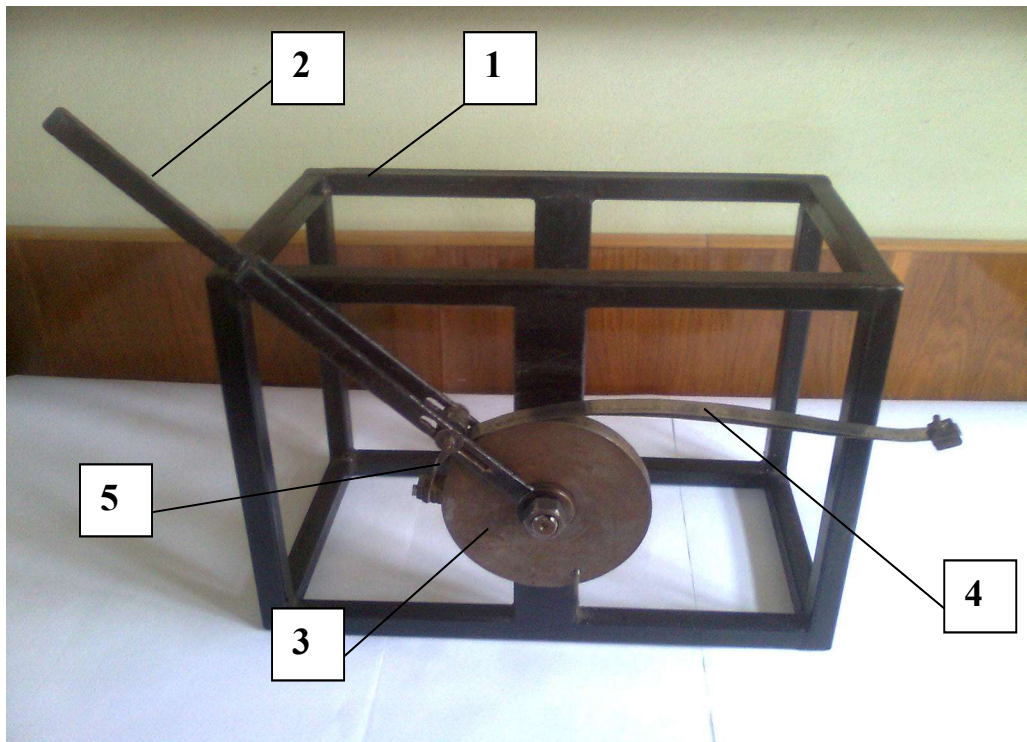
Гнутарний експериментальний лабораторний механізований пристрій:
